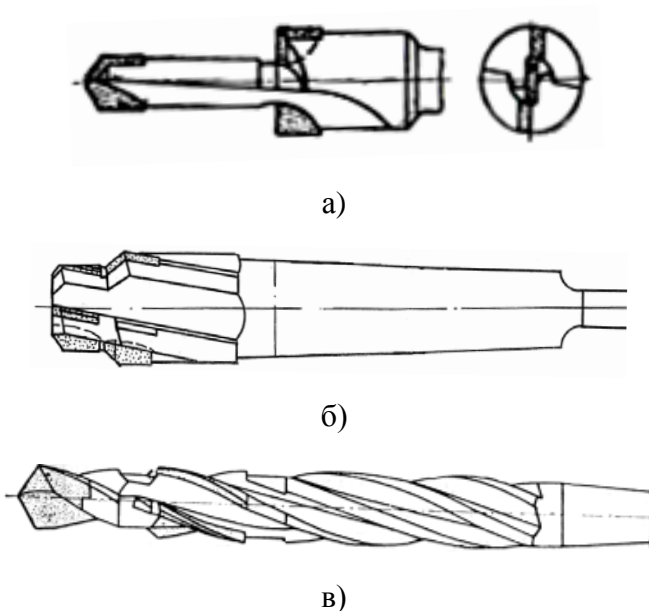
КОІ з напаяними пластинами: а – свердло-зенкер; б – двоступінчастий зенкер; в – свердло-розвертка
